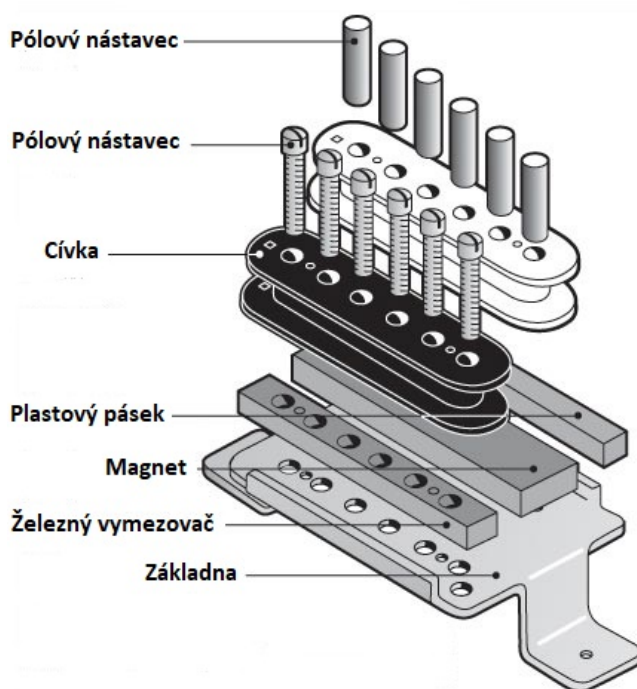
Konstrukce snímače typu single-coil, převzato s úpravami z [36]
